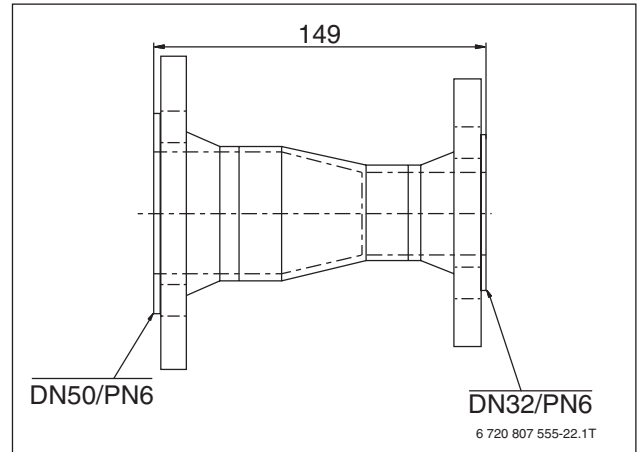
Anschlussstück DN 50/PN 6 – DN 32/PN 6 (Maße in mm)
